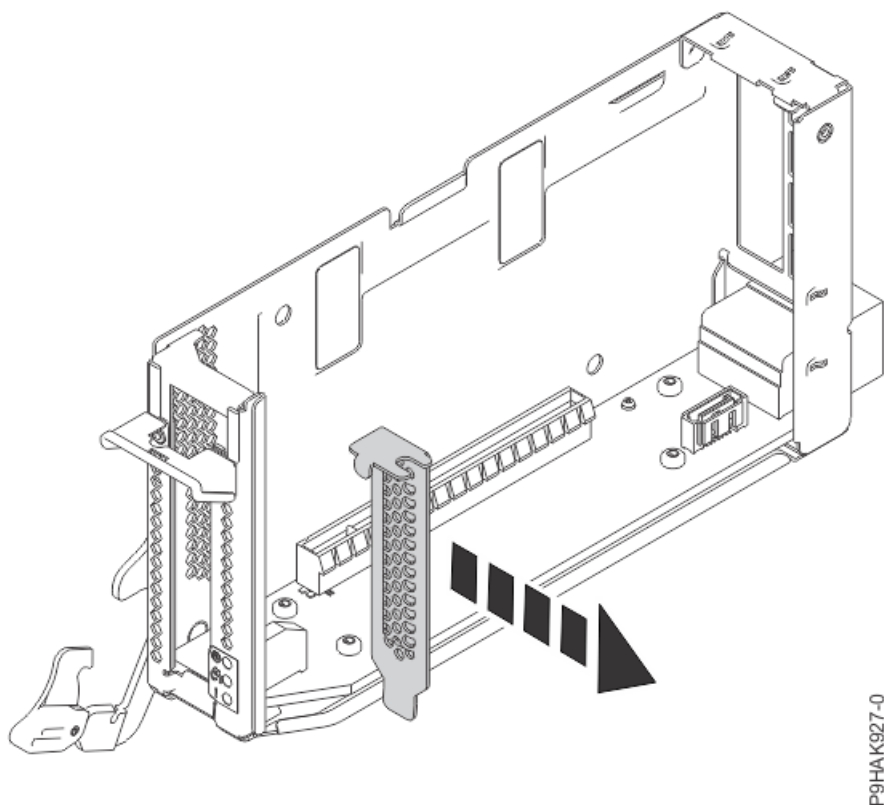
Extracció de la casset d'un panell de rebliment de contrapunta per al sistema 9080-M9S
